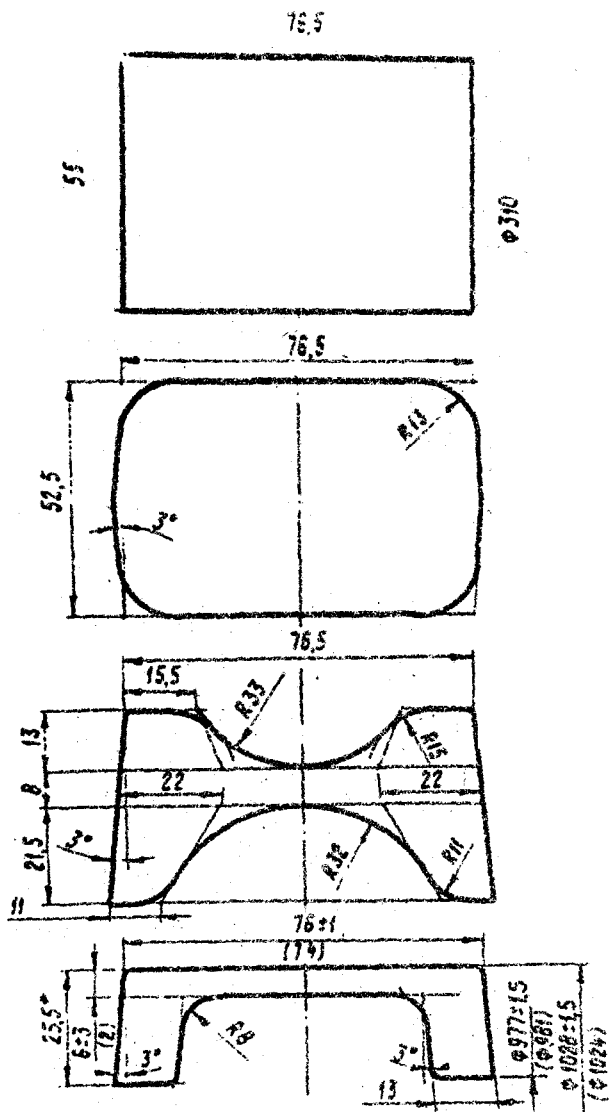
Калибровка заготовок промежуточного кольца компрессора из сплава ВТ20
